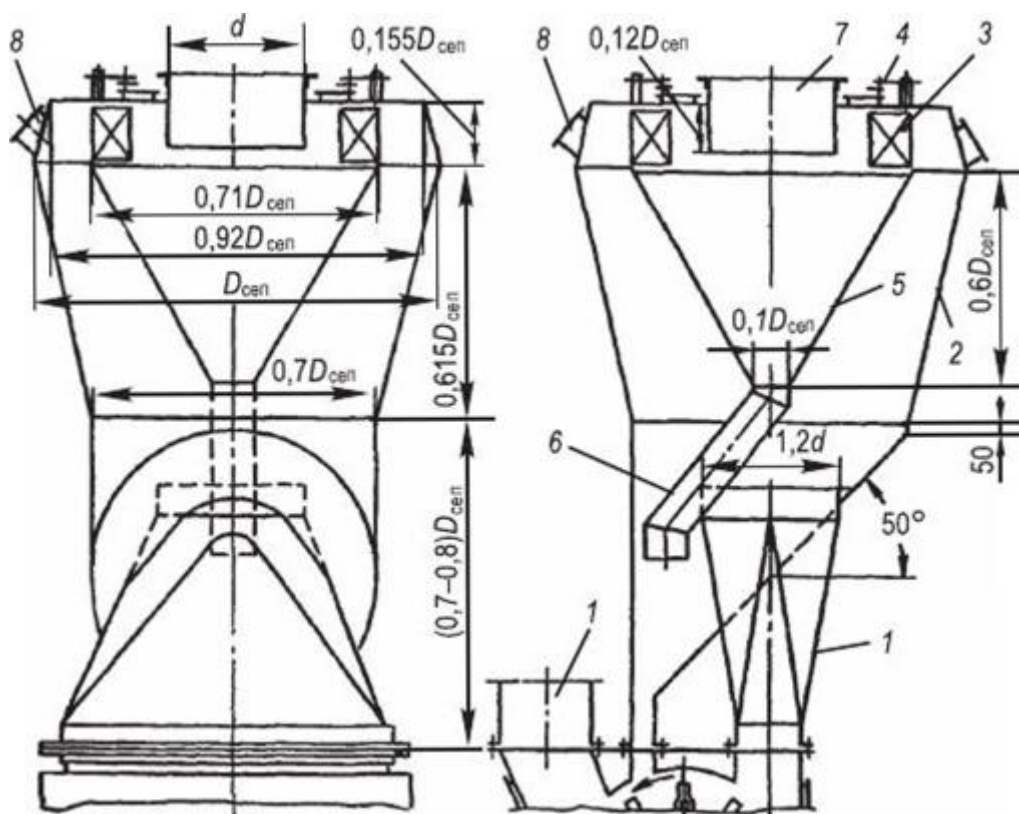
Відцентровий сепаратор для ММ [15]: 1 - Вхідний патрубков; 2 – зовнішній корпус; 3 – поворотні лопатки; 4 – привід поворотних лопаток; 5 - внутрішній конус; 6 - труба повернення; 7 вихідний патрубков; 8 - вибуховий клапан
